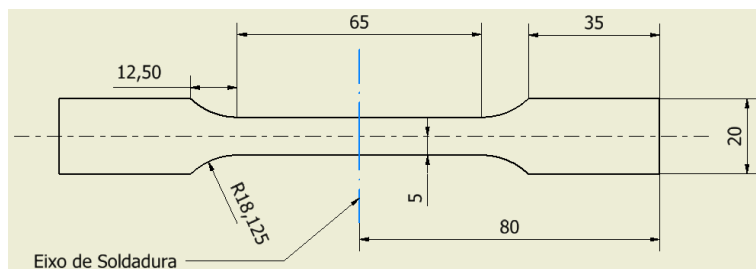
Geometria e dimensões do provete normalizado (dimensões em mm).
